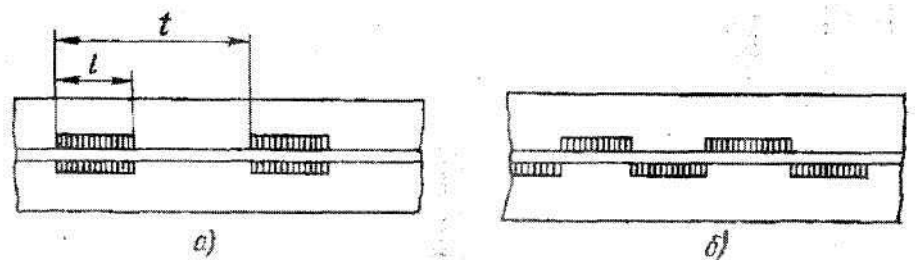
Типы сварных соединений и применяемые виды сварных швов при ручной дуговой сварке и сварке в защитных газах
